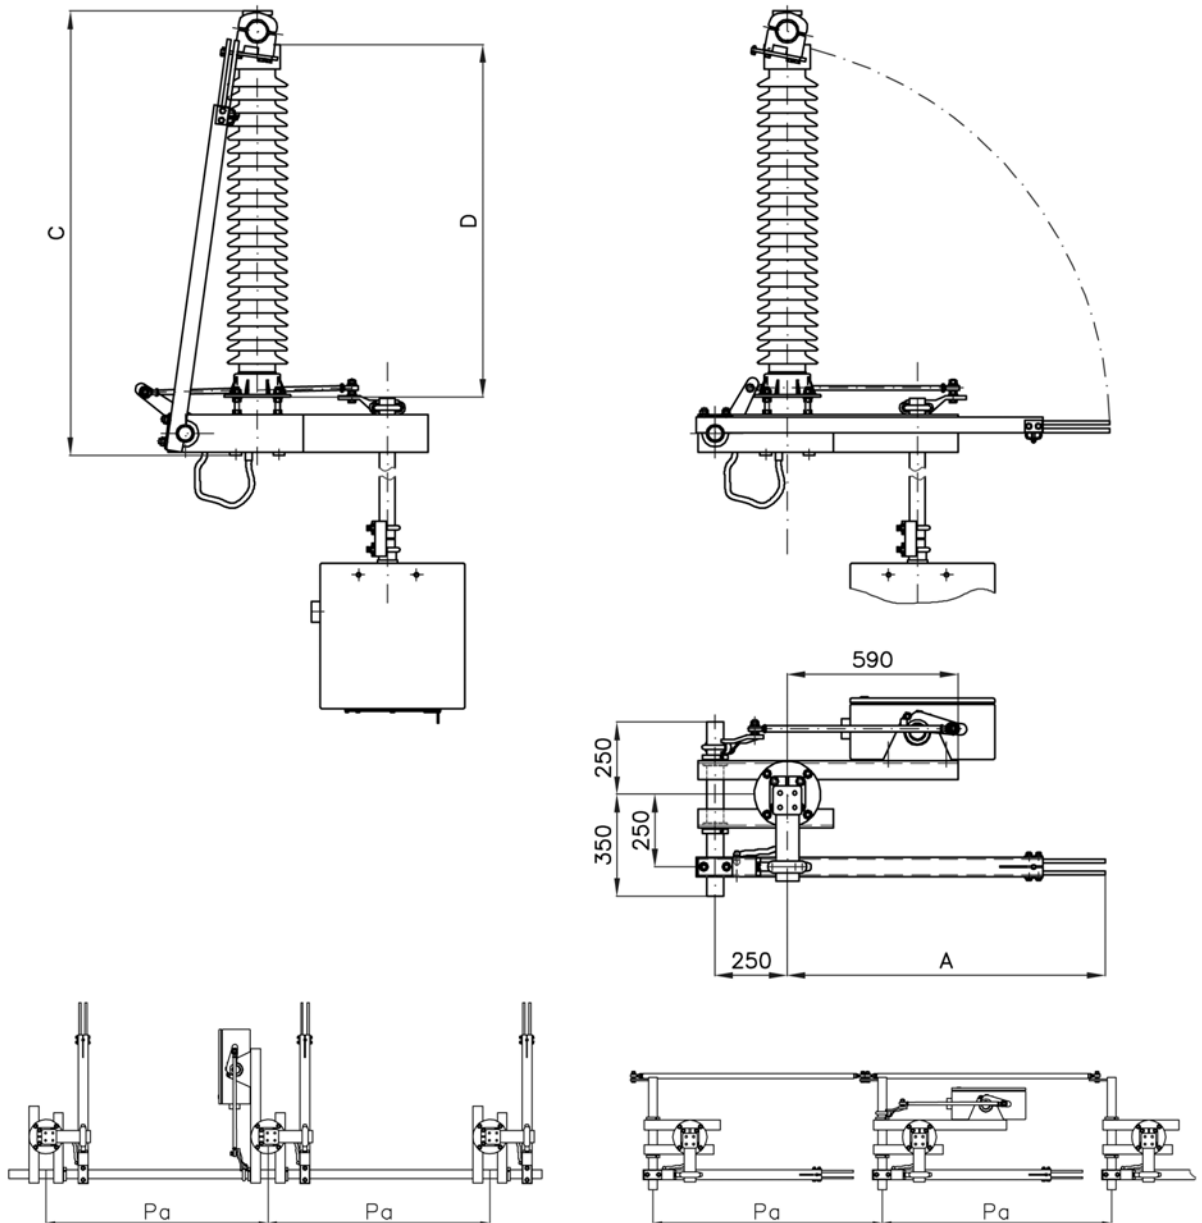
Grundabmessungen des Erdungsschalters Typ TEC
